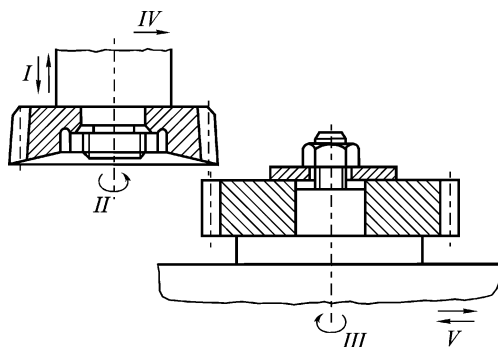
Схема нарезания зубчатого колеса долбяком
